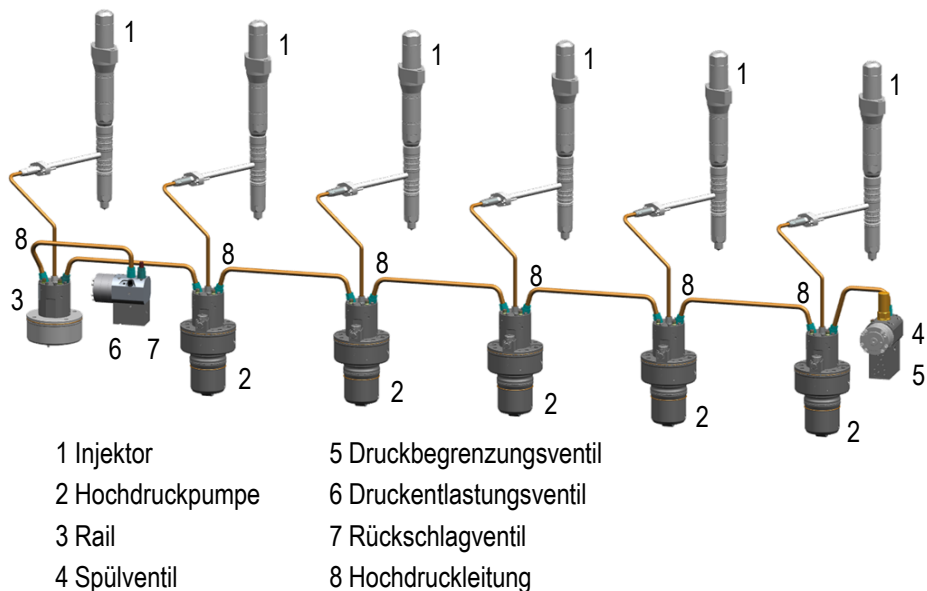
MAN CR2.2 Dieselmotorsystem für einen Reihensechszylindermotor
